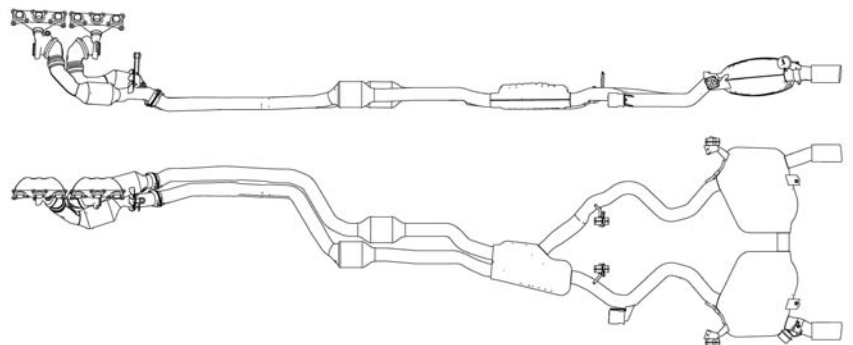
Abgassystem für den BMW-Reihensechszylinder-Ottomotor mit Twin-Turbo-Technik – der Mittelschalldämpfer weist das System als die Variante aus, wie sie im BMW-3er-Limousine und -Touring verbaut wird
